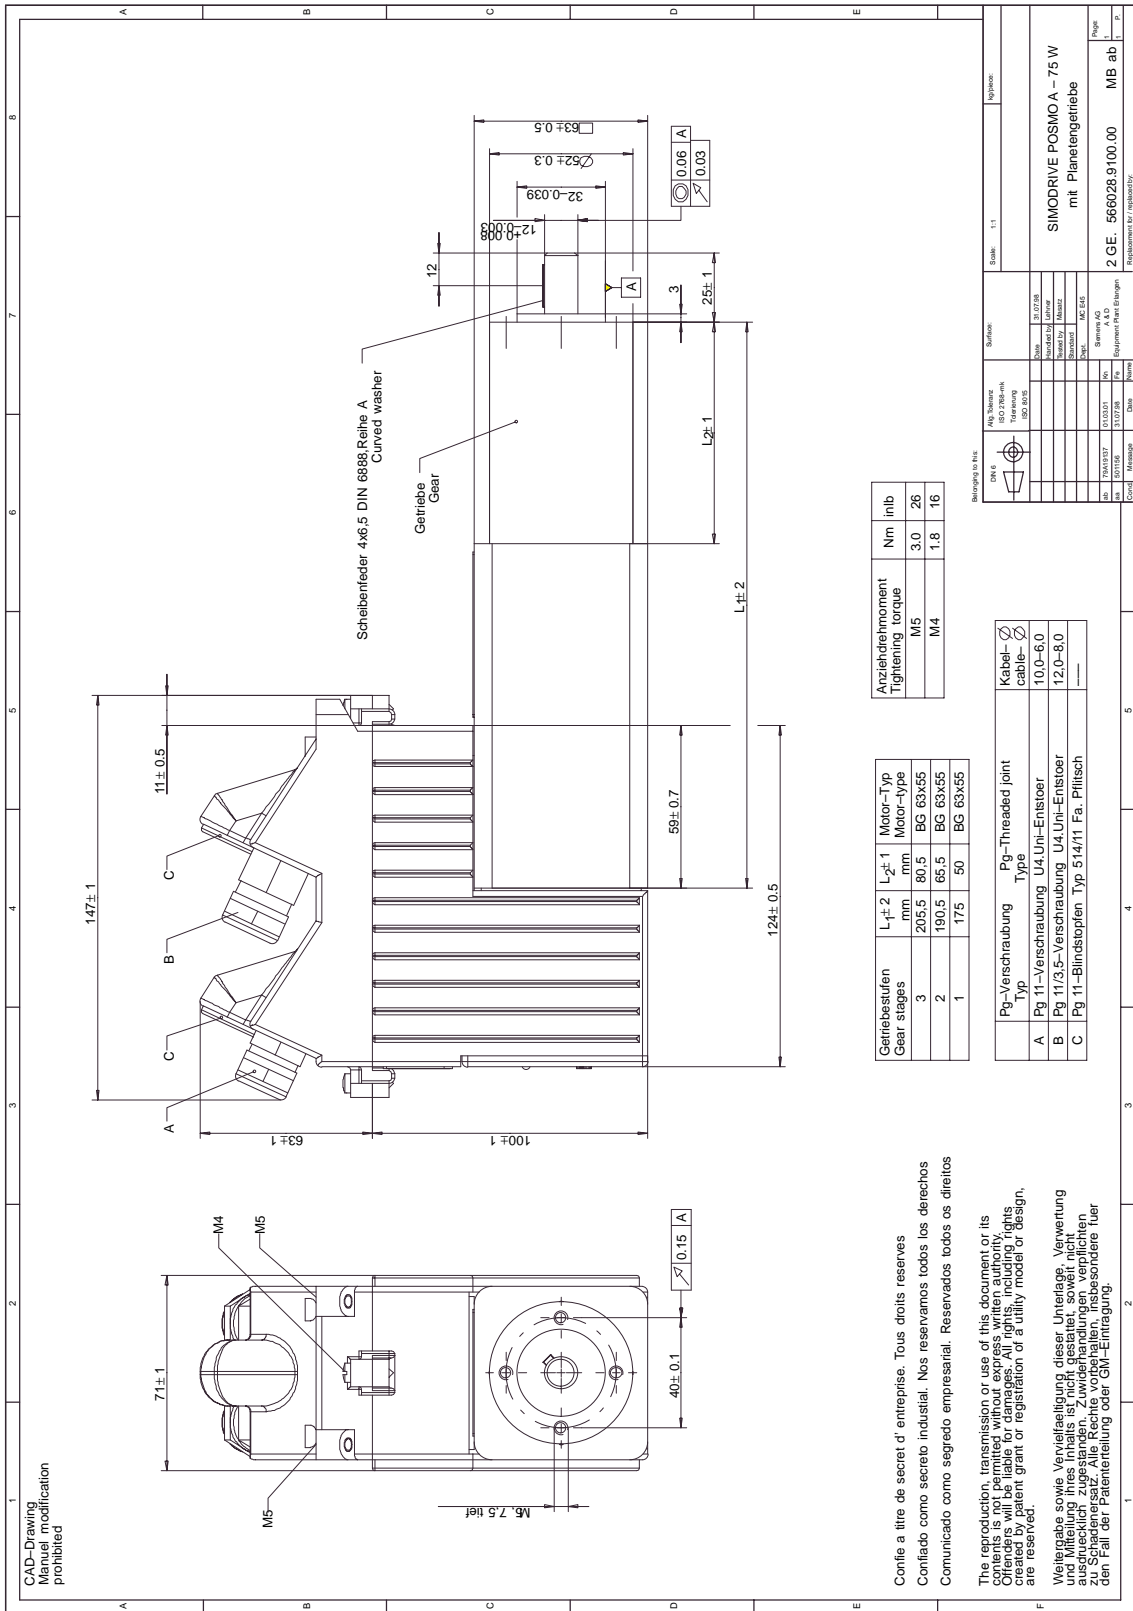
Maßblatt: SIMODRIVE POSMO A – 75 W mit Planetengetriebe
